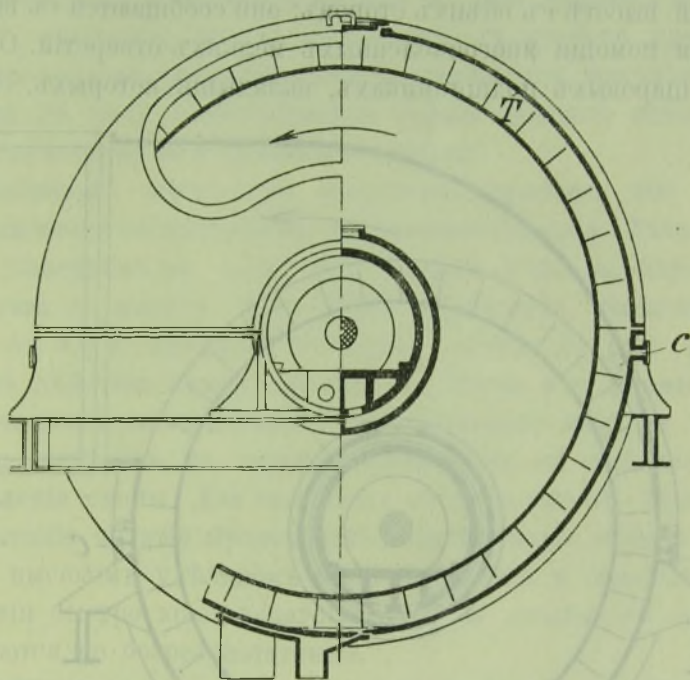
Продольный разръзъ черезъ центробъжный газоочиститель Theissen.
